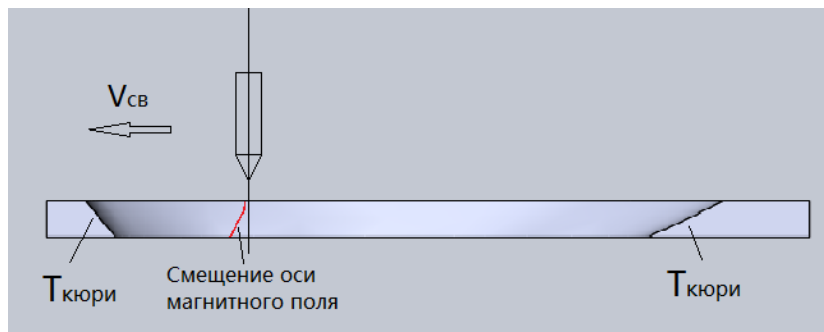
Смещение оси магнитного поля при дуговой сварке магнитных металлов [Displacement of the axis of the magnetic field during arc welding of magnetic metals]
